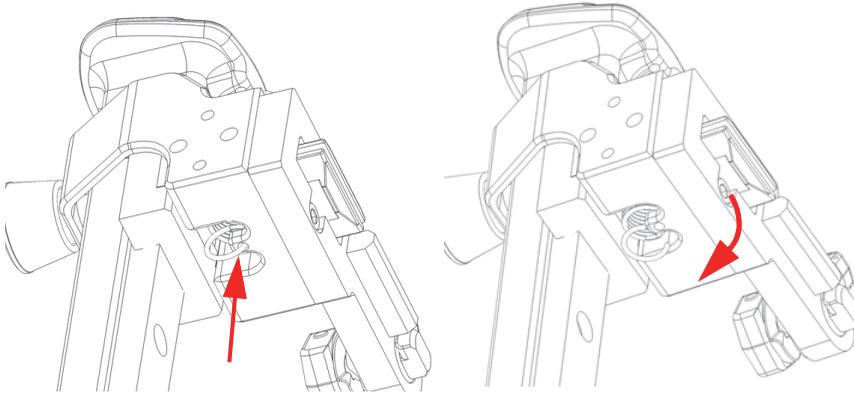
Sprungfeder aus der Bohrung entfernen
